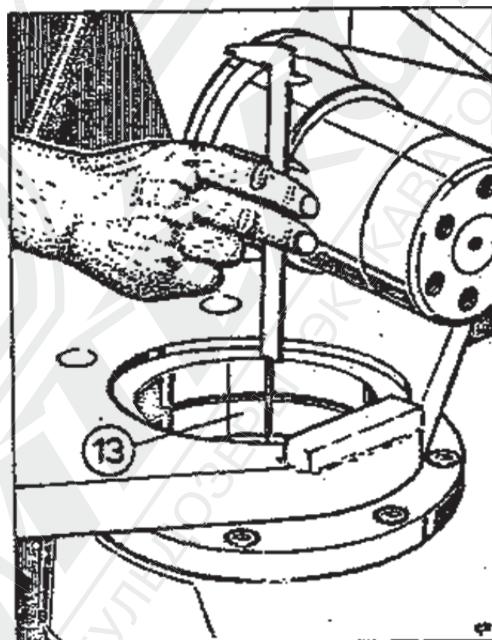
Измерение расстояния между дорожкой подшипника и верхним листом корпуса
